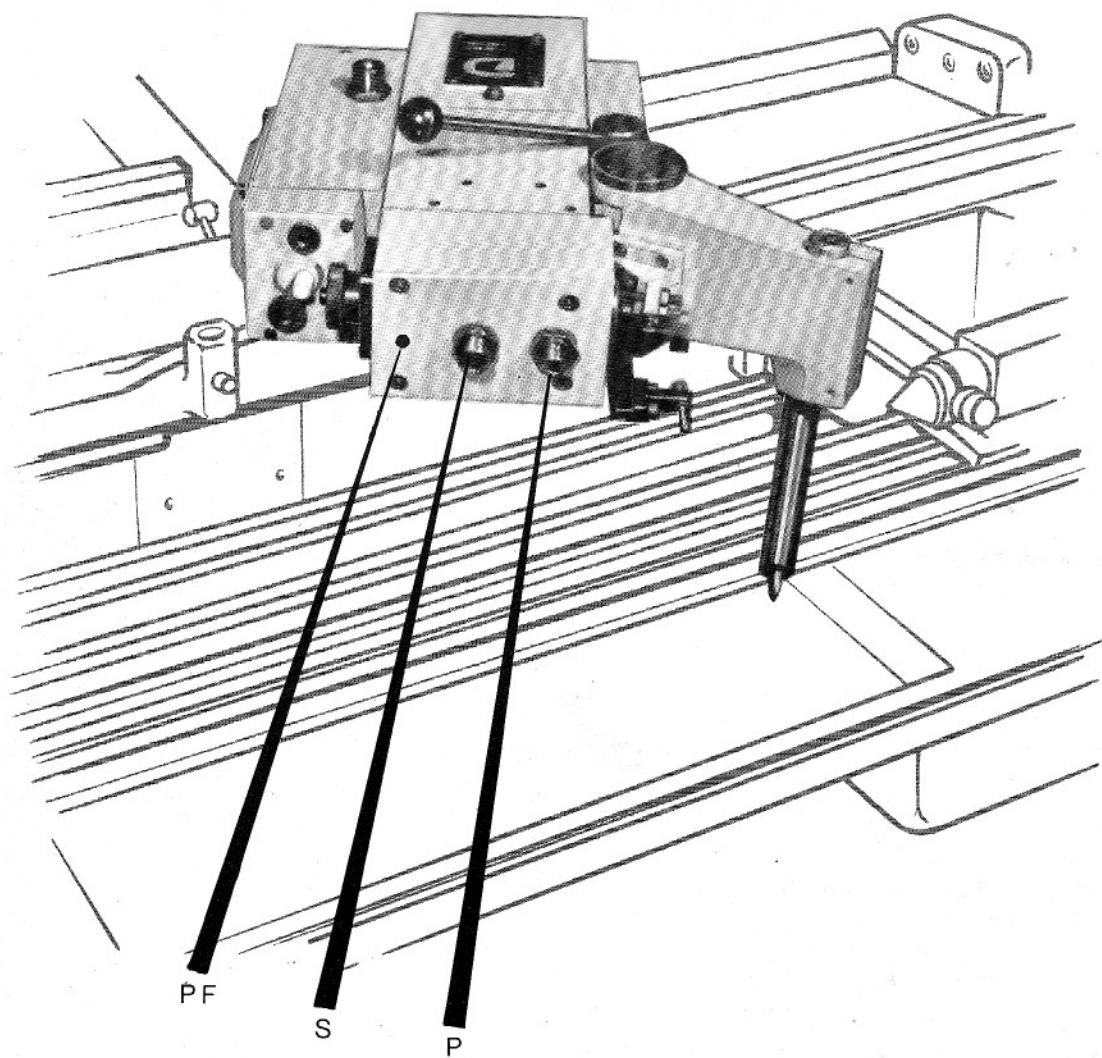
Branchement des tuyaux flexibles sur le copier
